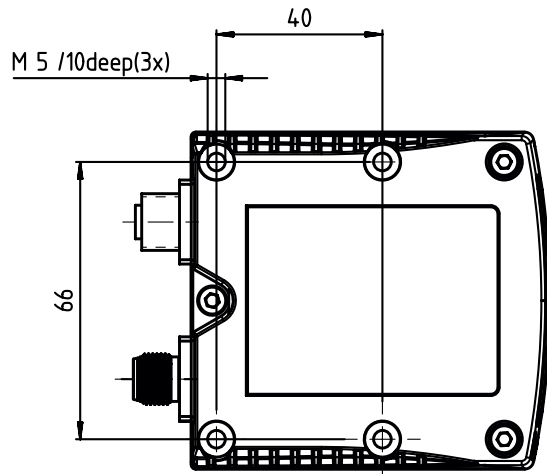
Trous de fixation sur la face inférieure de l'appareil
